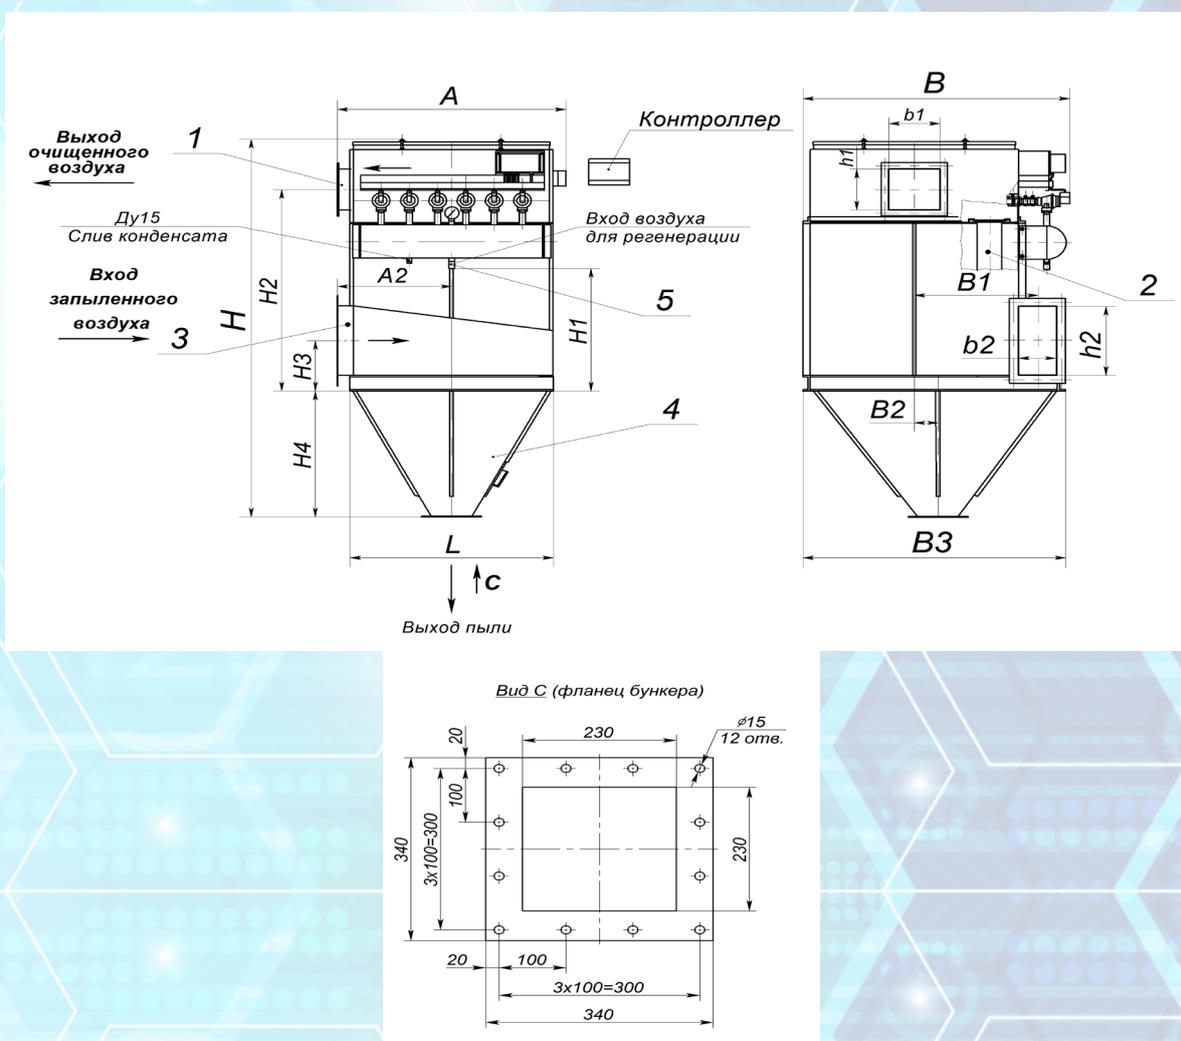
Схема фильтров рукавных типа ФРИП-5; ФРИП-10; ФРИП-15; ФРИП-30; ФРИП-180
